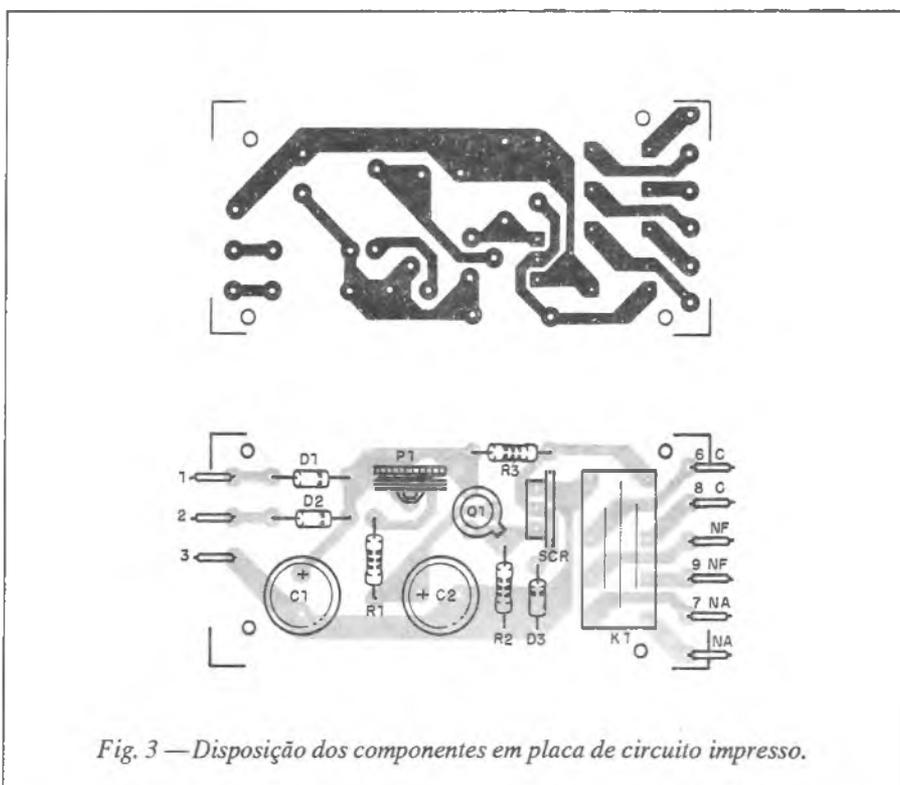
Disposição dos componentes em placa de circuito impresso.
